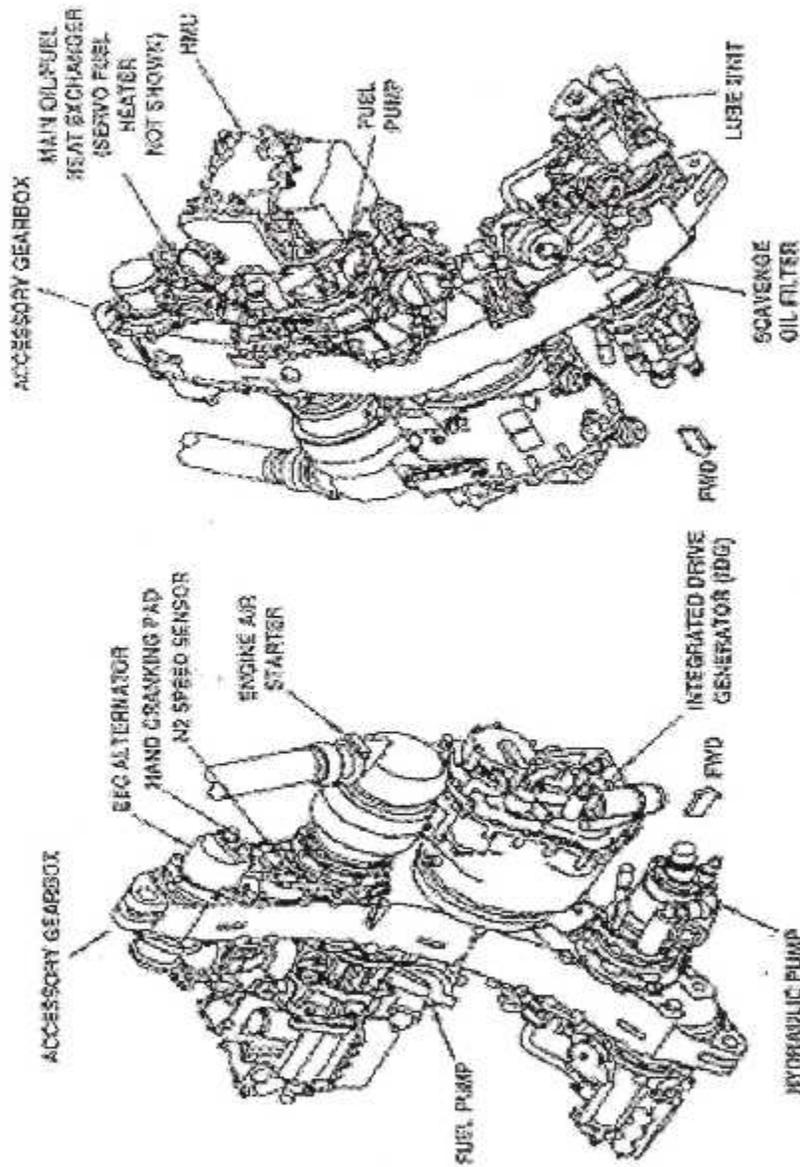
LES ACCESSOIRES DE LA GEARBOX (MODULE AGB).
